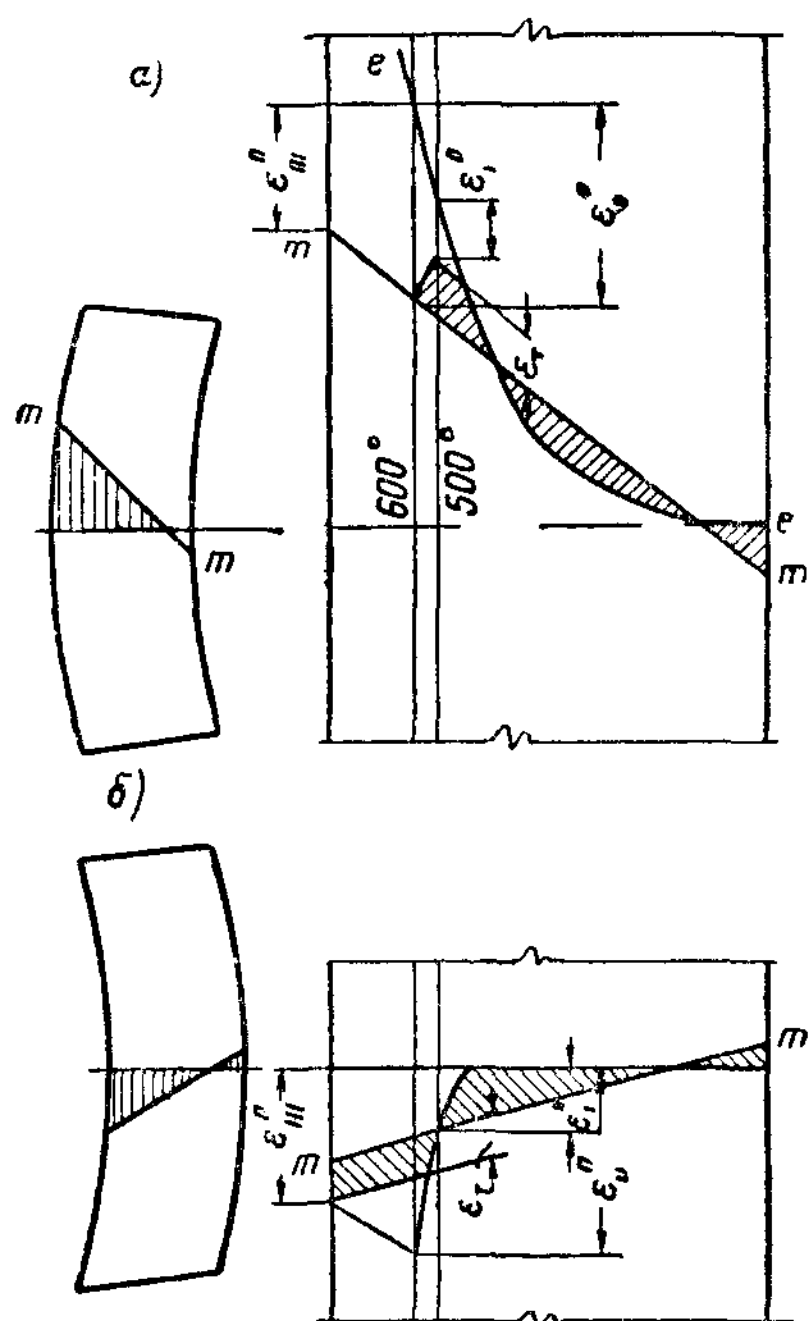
Эпюры сварочных напряжений при наплавке валика на кромку полосы
